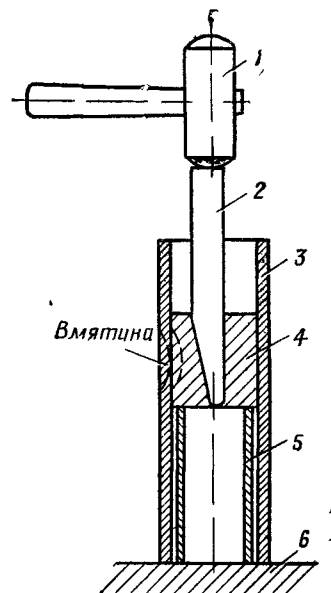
Правка вмятины с использованием разжимного приспособления:
